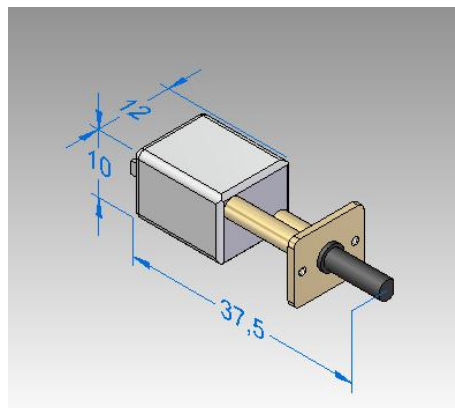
Dibujo CAD del motor con sus dimensiones principales (mm).
